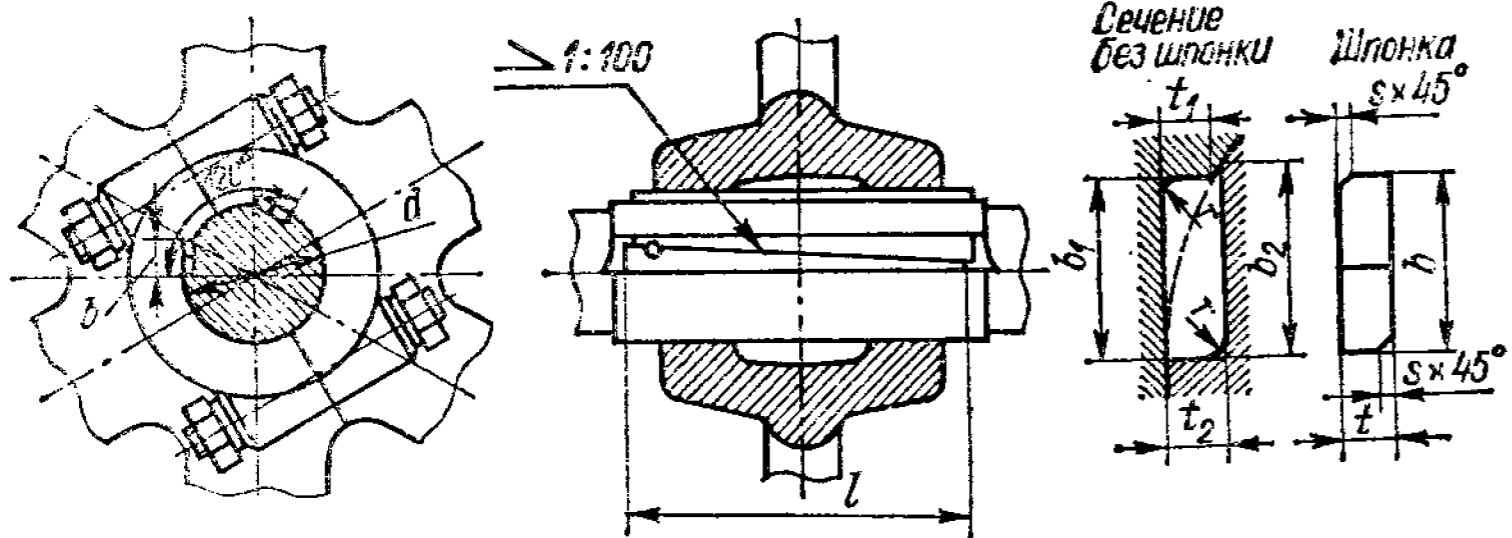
Размеры сечений пазов для клиновых шпонок
